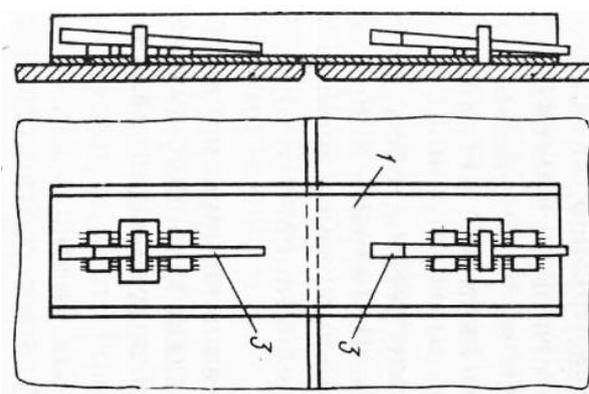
Схема крепления швеллера к листовой конструкции
